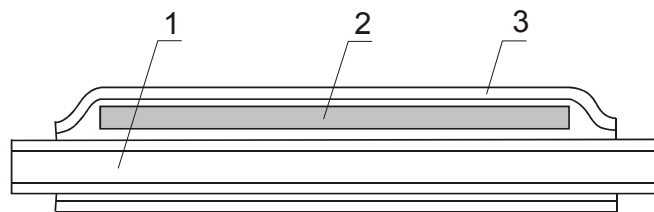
Комплект деталей для захисту місця зварювання:
